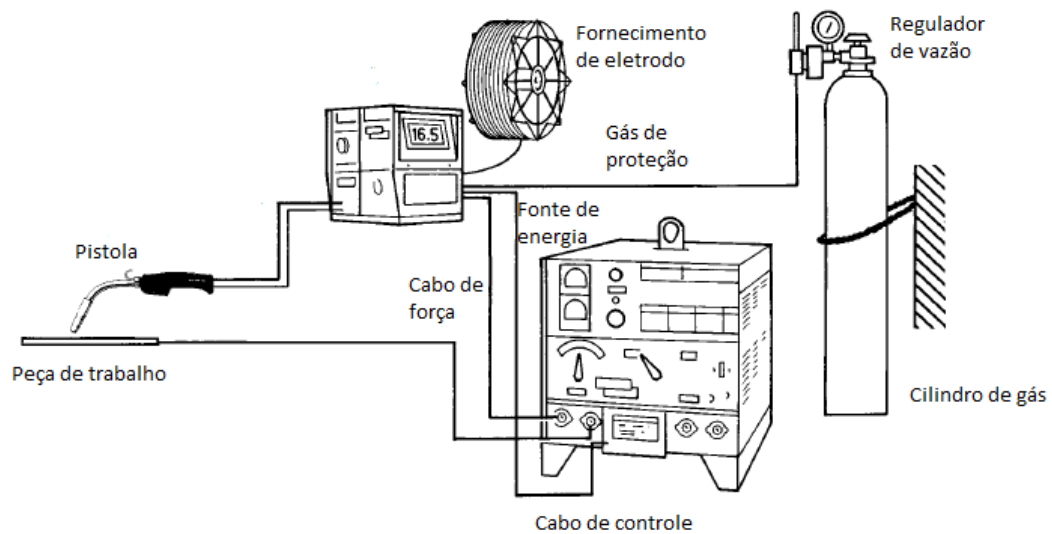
Equipamento básico para soldagem semi-automática GMAW
